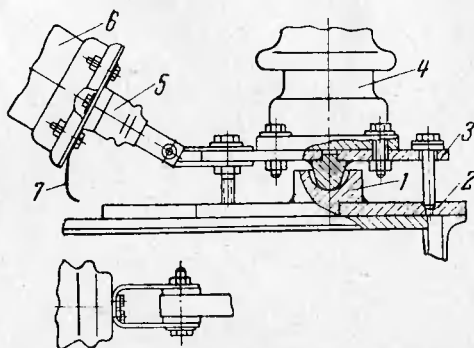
Конструкция изоляции нижних фланцев первых искрового и вентильного рабочих элементов.
